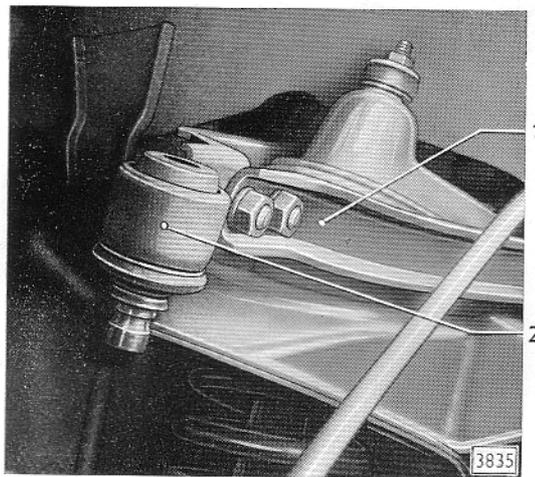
Befestigung Führungsgelenk am oberen Lenker
